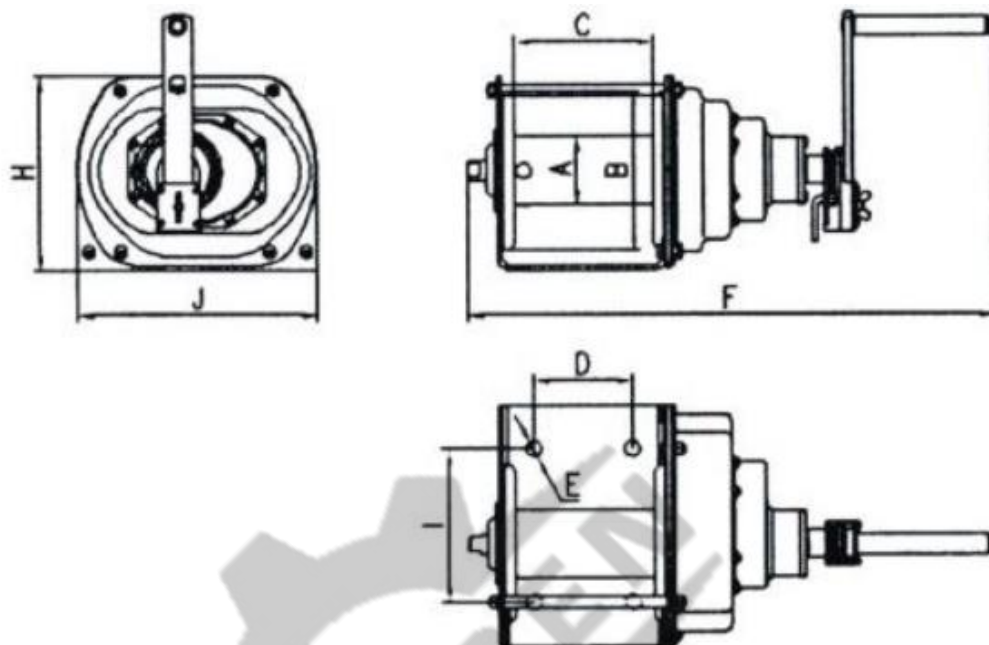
Габаритные размеры лебедки ручной канатной GEARSEN JHW
